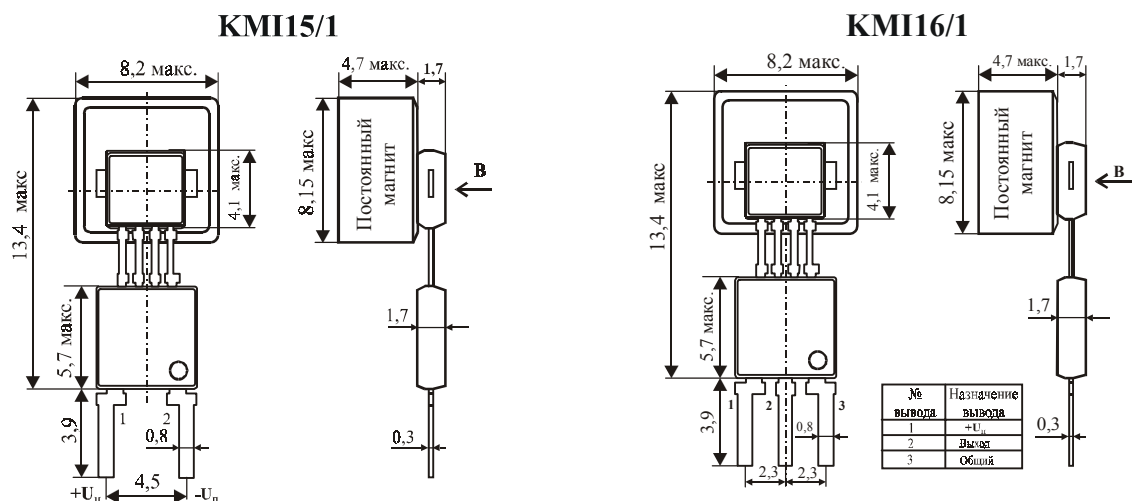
Внешний вид и габаритные размеры датчиков типа КМ15/1, КМ16/1
